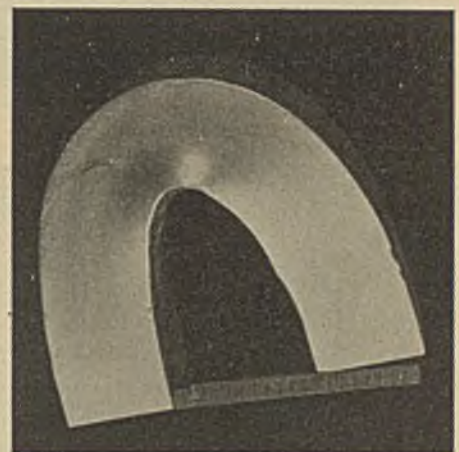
Biegeprobe einer Schweißnaht (Blechstärke 88 mm).
